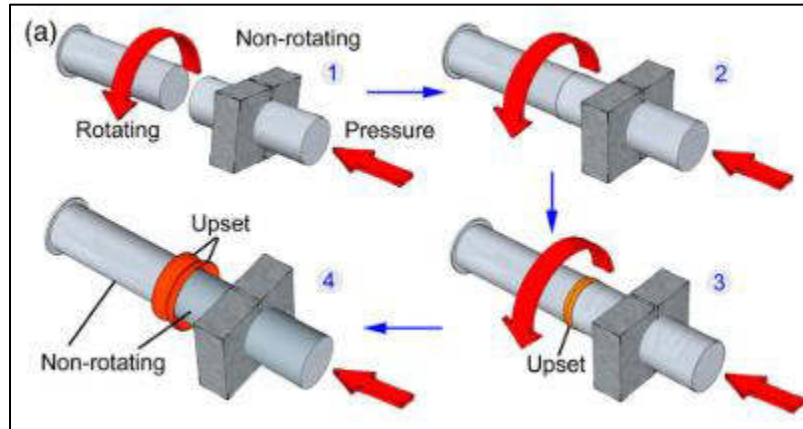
Principio del funcionamiento de la soldadura por fricción [63]
